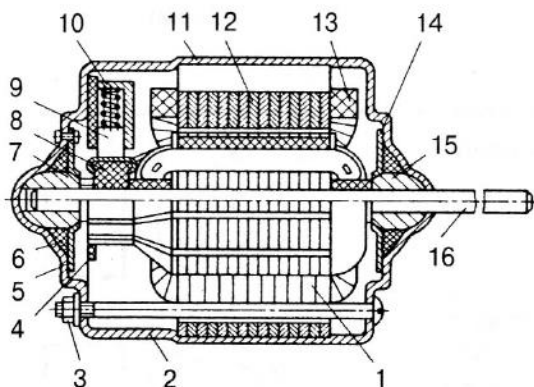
Электродвигатель с электромагнитным возбуждением: 1 – якорь; 2 – крышка; 3 – винт; 4 – траверса; 5,14 – плоские пружины; 6 – сальник; 7, 15 – подшипники; 8 – коллектор; 9 – щетки; 10 – щеткодержатель; 11 – корпус; 13 – обмотка возбуждения; 16 – выходной вал
